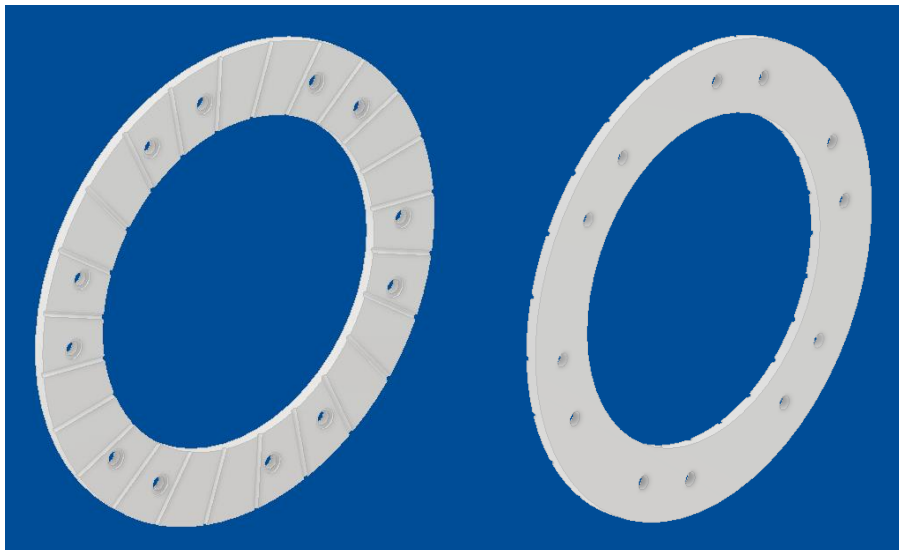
a. Disque d'embrayage à étudier en vue de face et arrière
